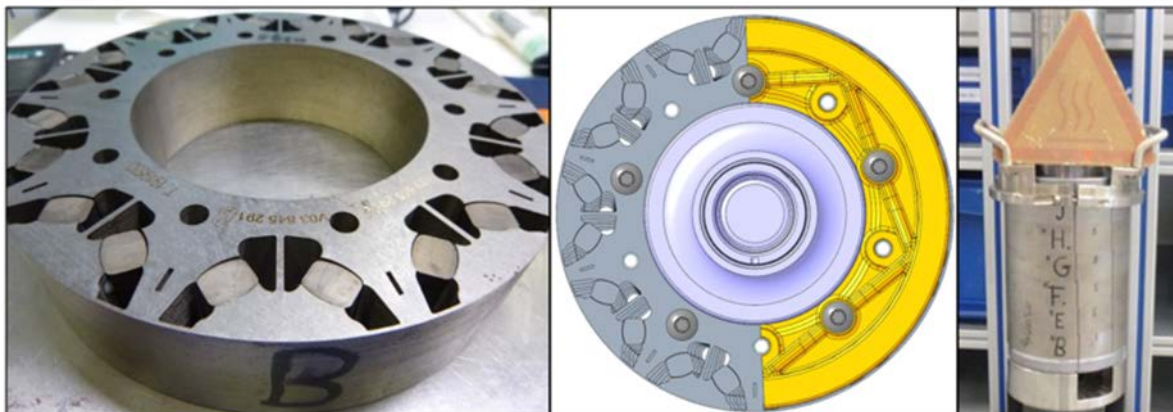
Fertiges Lamellenpaket (links), Schrägung des Rotors (Mitte), gefügter Rotor (rechts)
